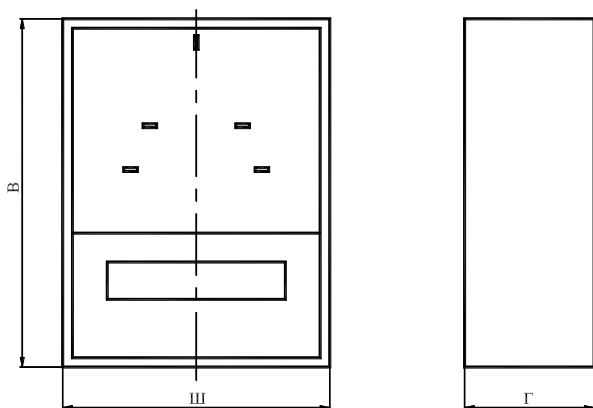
Габаритные размеры корпусов металлических ЩУРН
